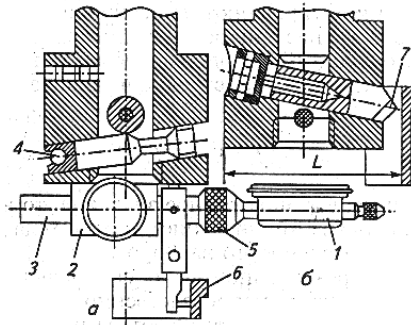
Резцовая головка с приспособлением для центрирования гильз (а) и установки резца (б): 1 – индикатор; 2 – колодка; 3 – державка; 4 – установочный механизм с шариком; 5 – цанговый зажим; 6 – рычаг; 7 – резец.
